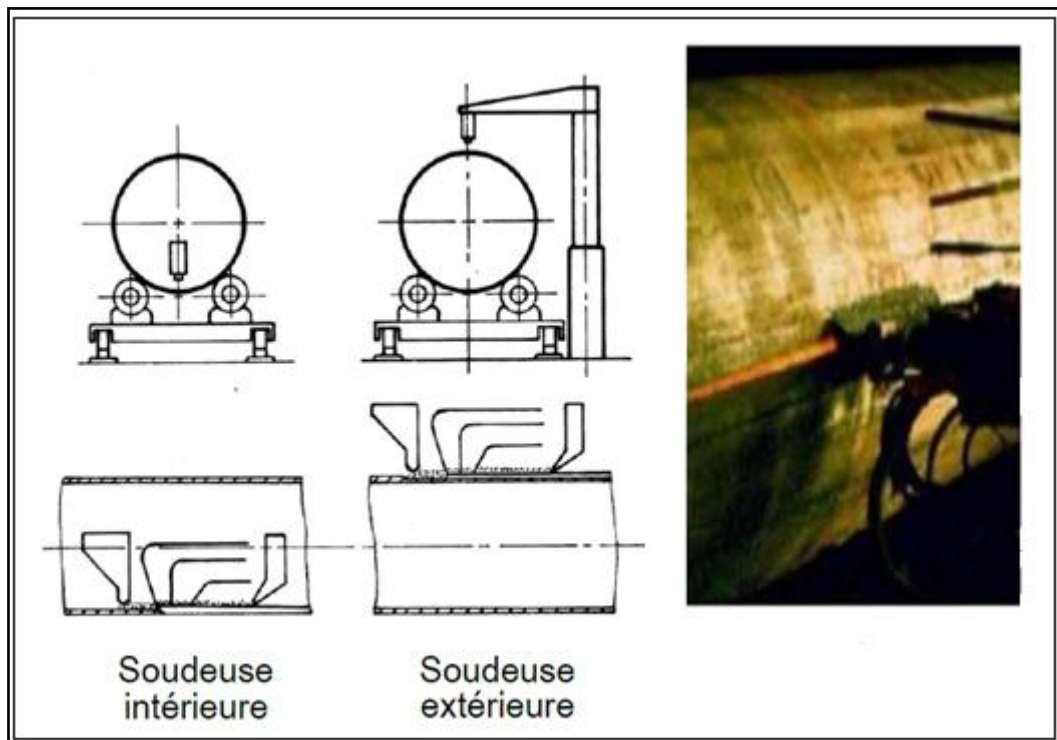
Soudage des tubes par le procédé « UOE », [4]
